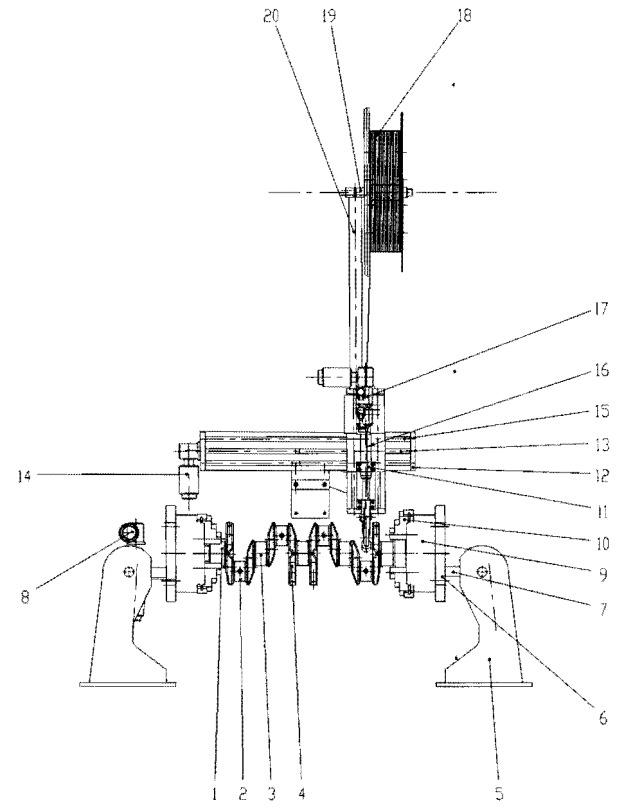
Vedere frontală a dispozitivului de încărcare prin sudare a arborilor din industria auto conform invenției, cu arborele prins în MPR;
